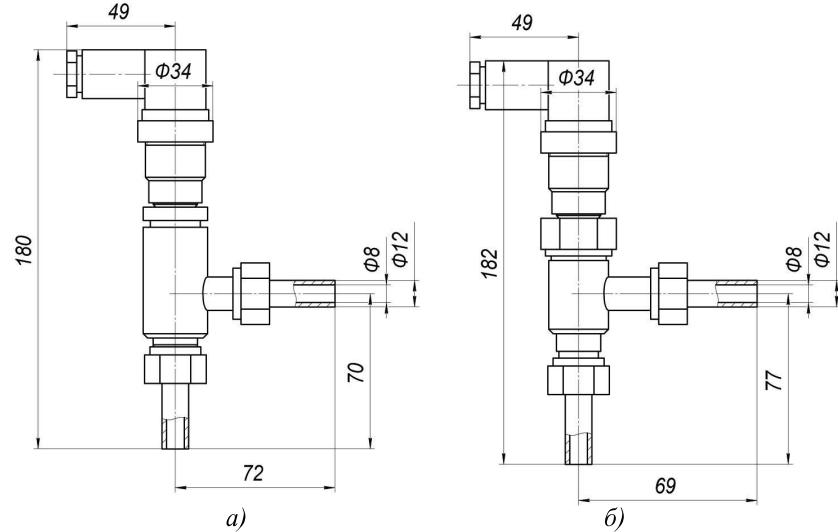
Габаритные и монтажные размеры проточного пассивного датчика
